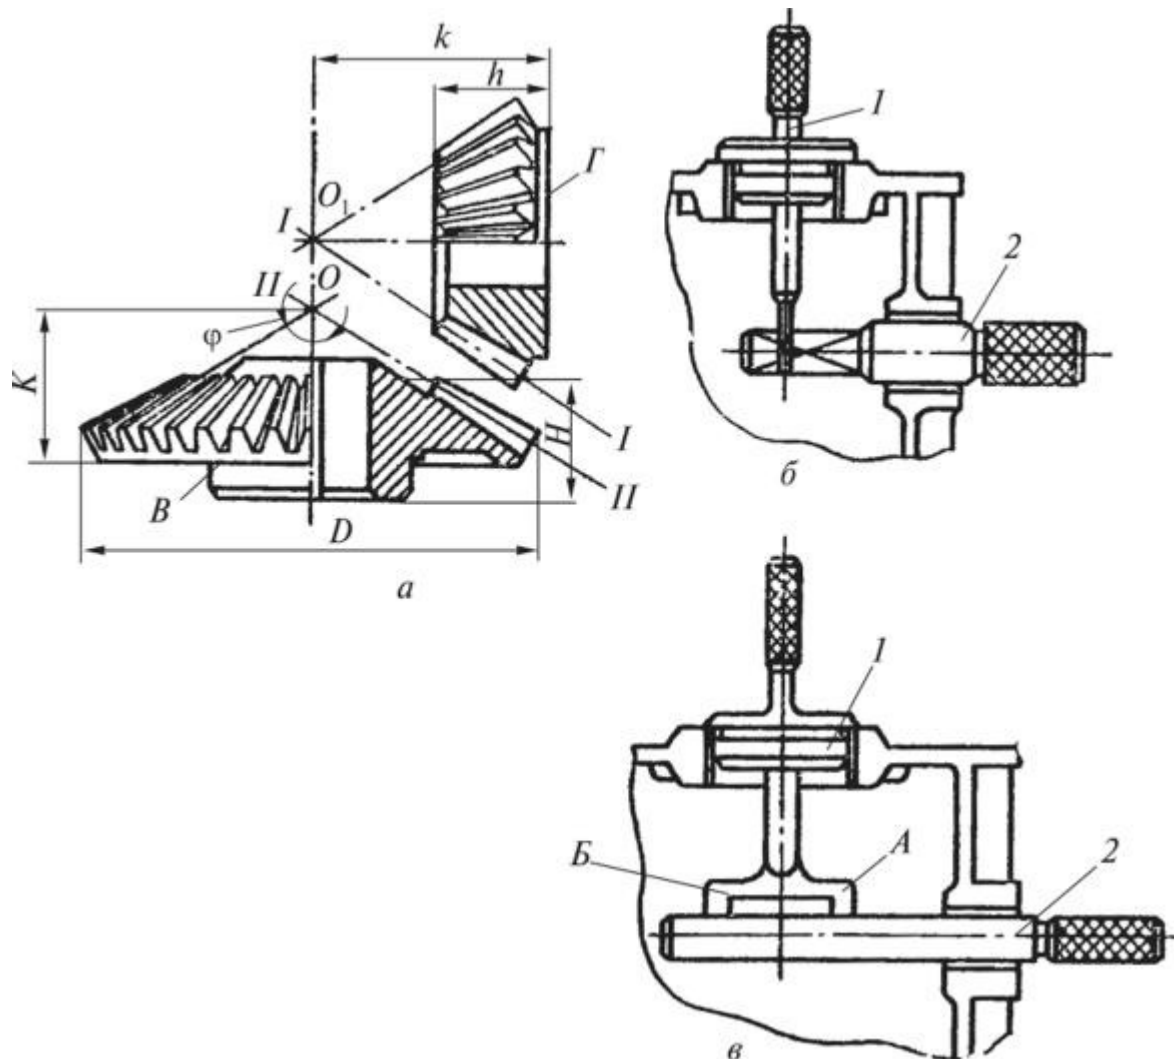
Схемы передачи с коническими зубчатыми колесами (а), проверки взаимного расположения отверстий для валов (б), проверки перпендикулярности осей валов (в): D — наружный диаметр колеса, H — высота большого колеса; h — высота малюю колеса; φ — угол начального конуса
